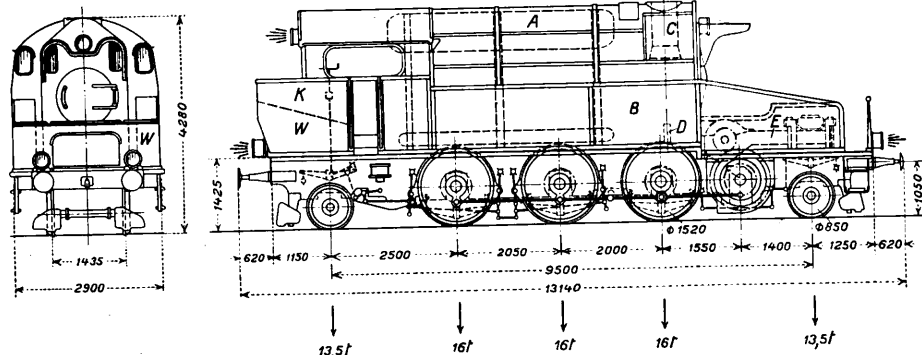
Typenskizze der Hochdruck-Lokomotive „Winterthur“. — Maßstab 1:150. A obere Kesseltrommel, B Rauchkammer, C Kamin, D Blasrohr, E Dampfmotor, F Vorgelegewelle, K Kohle, W Wasser.
